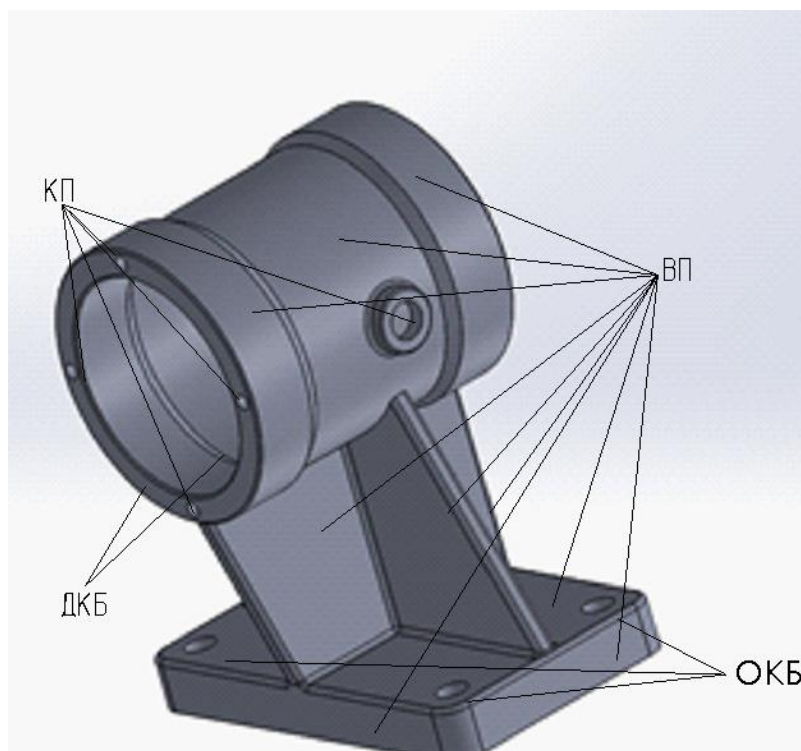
Класифікація поверхонь деталі «Корпус».
